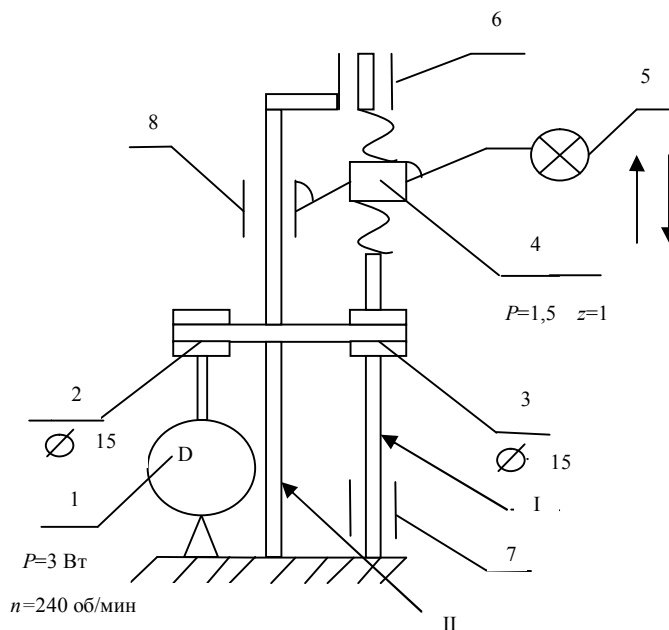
Кинематическая схема подъёма (опускания) источника излучения: I – резьбовой вал; II – стойка; 1 – двигатель; 2 – шкив ведущий 15 мм; 3 – шкив ведомый; 4 – гайка; 5 – источник излучения; 6 – подшипник верхний; 7 – подшипник нижний; 8 – направляющая втулка
